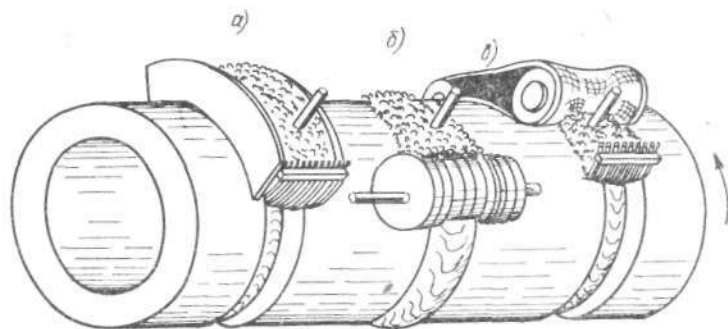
Устройства для удержания флюса при сварке кольцевых швов малого диаметра: а — коробочка; б — катки; в — гусеница.
